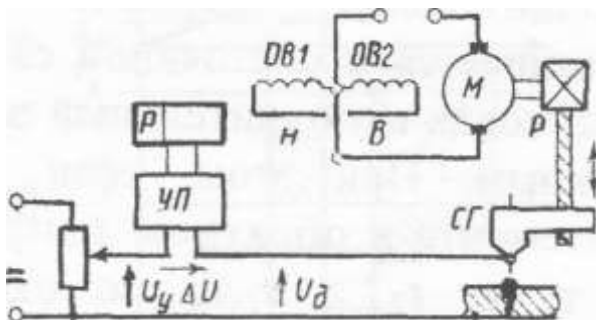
Схема релейного регулювання зварювальної дуги
